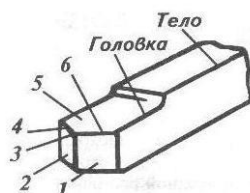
Элементы резца: 1 – главная задняя поверхность; 2 – вспомогательная задняя поверхность; 3 – вершина резца; 4 – вспомогательная режущая кромка; 5 – передняя поверхность; 6 – главная режущая кромка
